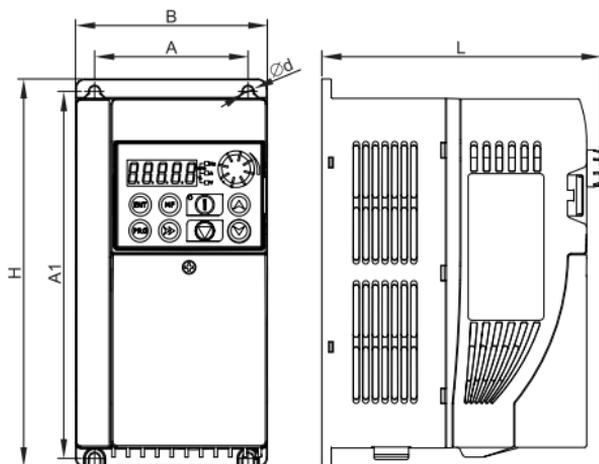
Габаритные и установочные размеры преобразователя (габариты 2, 3)
